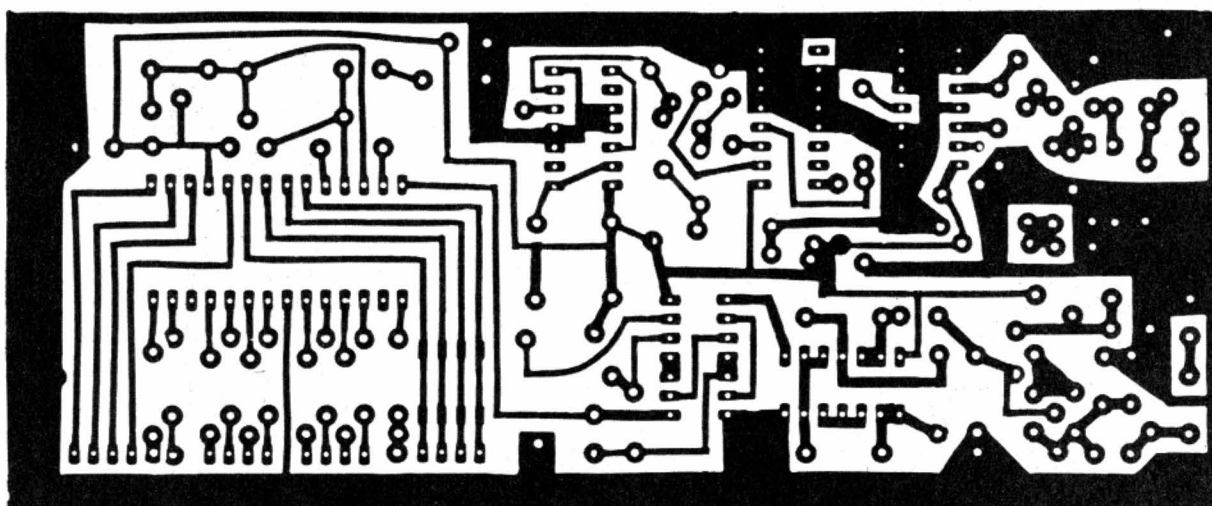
Dessin du circuit imprimé et implantation des composants. Version modifiée pour SP1660B en remplacement du SP1023.
